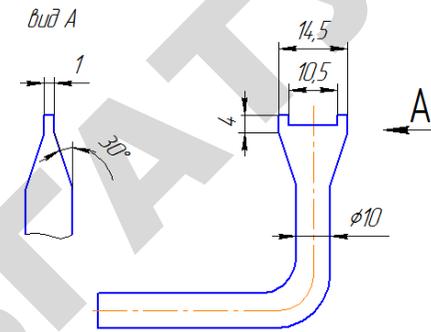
Специальная отвертка для разборки и сборки клапанов бустера
